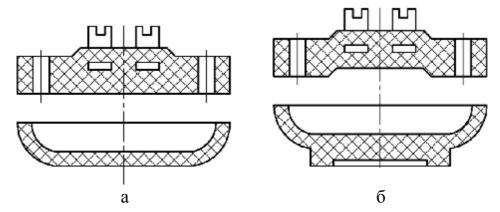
Опорные поверхности конструкций изделий: а – нетехнологичные; б – технологичные
